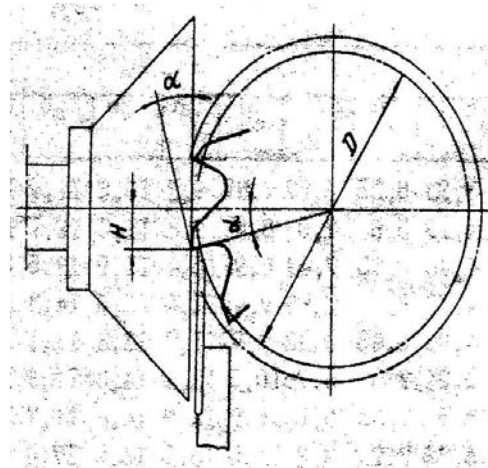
Установка упорки при заточке зуба фрезы по задней поверхности
